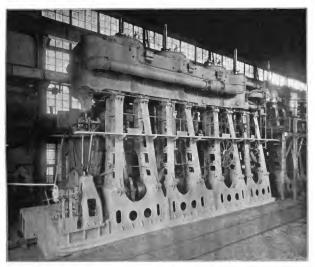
Eine der beiden Hauptmaschinen für "Kaiser Wilhelm den Großen" in der Werkstatt der Stettiner Maschinenbau-A.-G. "Vulcan", Bredow bei Stettin.
